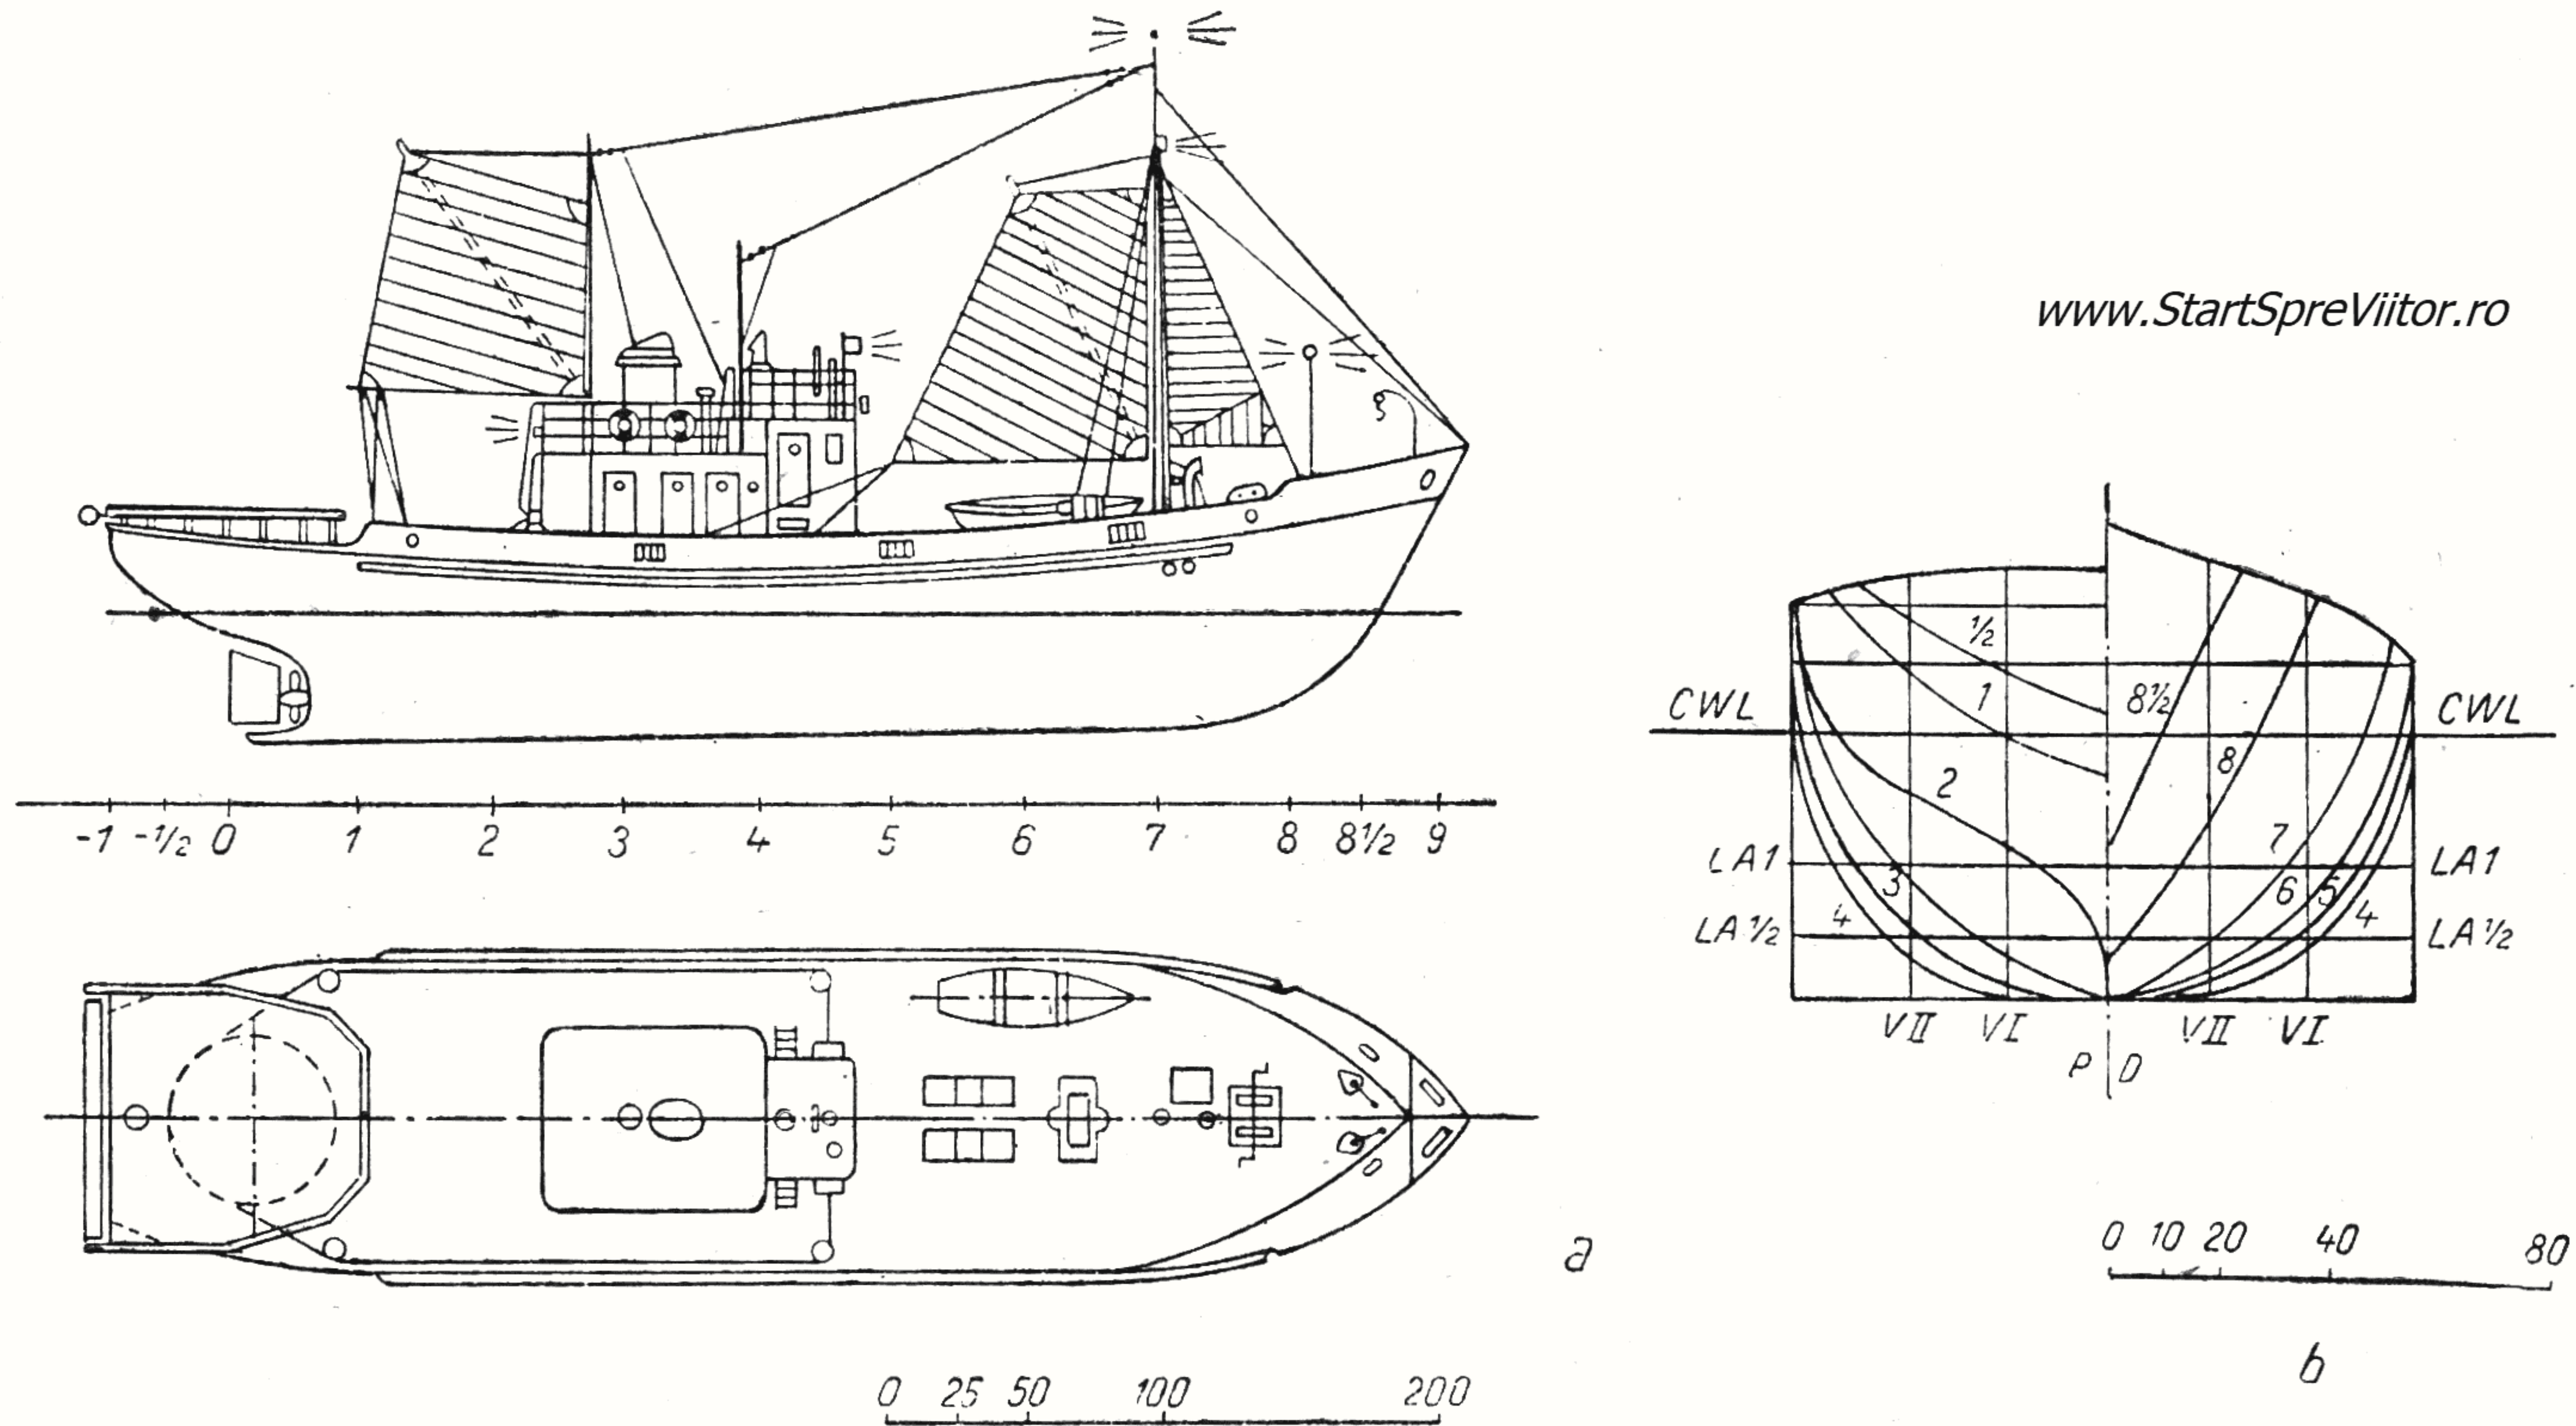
Modelul pescadorului „Pălămida“: a) plan general de construcție; b) plan de forme transversal.
